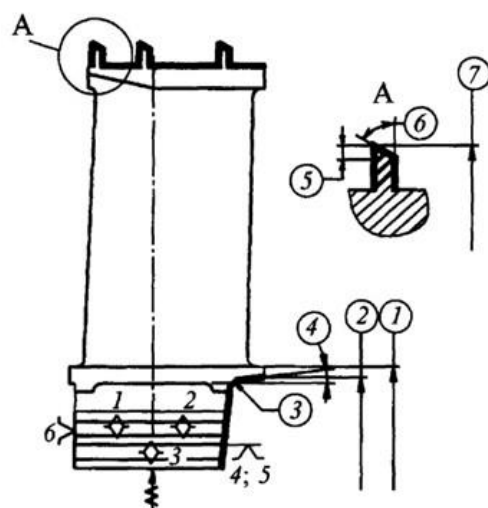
схема базування лопатки під час обробки циліндричних поверхонь.
